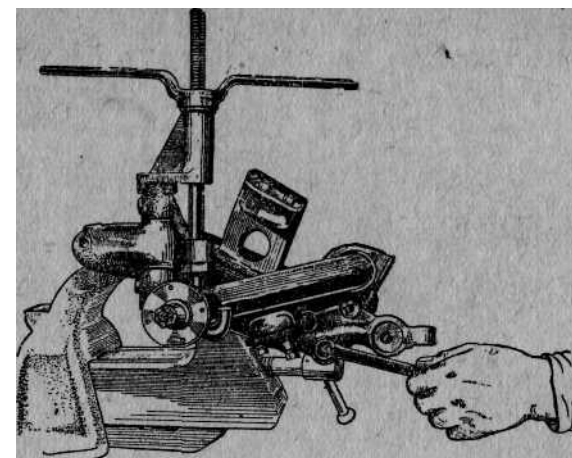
Сжатие пружины подвески при помощи приспособления.
